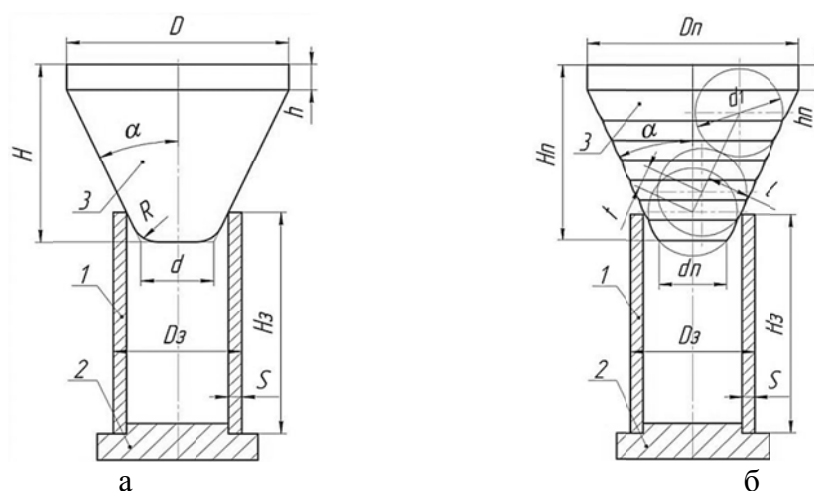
Схемы процессов открытой раздачи трубчатых заготовок (1 – заготовка, 2 – плита, 3 – пуансон):
